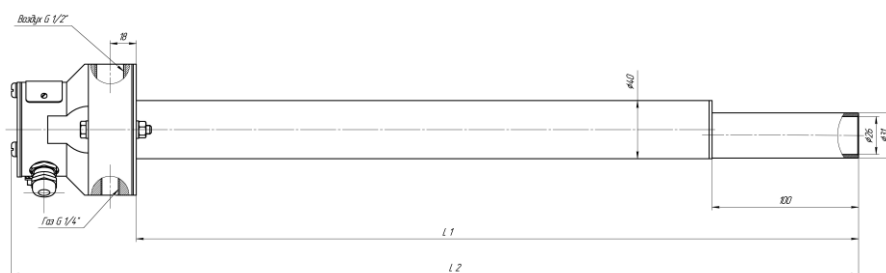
Габаритные размеры горелок газовых 3ЗГ-ВТ 2
